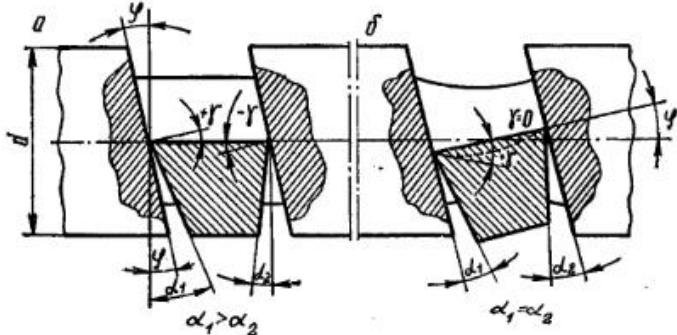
Установка чистовых (а) и черновых (б) резцов при нарезании ходовых резьб
